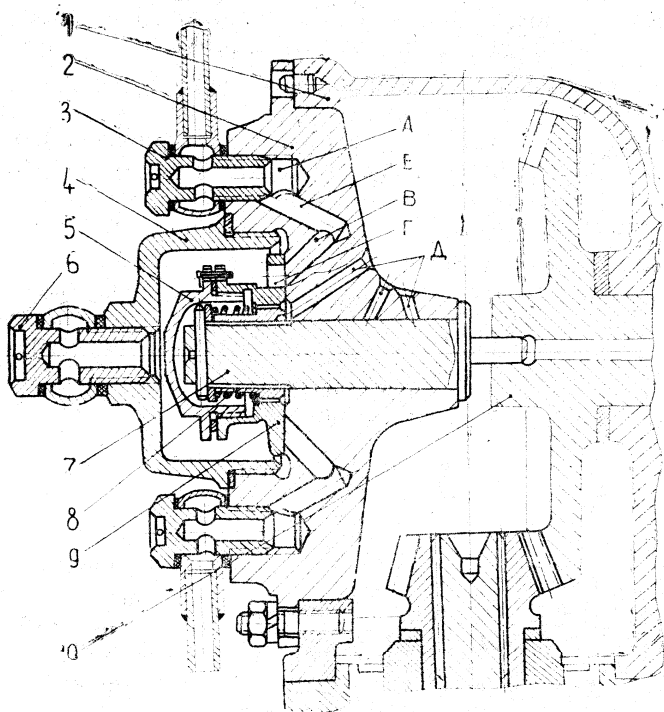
Воздухораспределитель: 1 — корпус привода топливного насоса; 2 — корпус воздухораспределителя; 3, 6 — зажимы; 4 — колпак; 5 — крышка распределительного диска; 7 — валик воздухораспределителя; 8 — регулировочная шлицевая муфта; 9 — распределительный диск; 10 — шестерня привода топливного насоса; А — резьбовые отверстия; Б, В — косые сверления; Г — овальное отверстие; Д — сверления для смазки валика и диска
